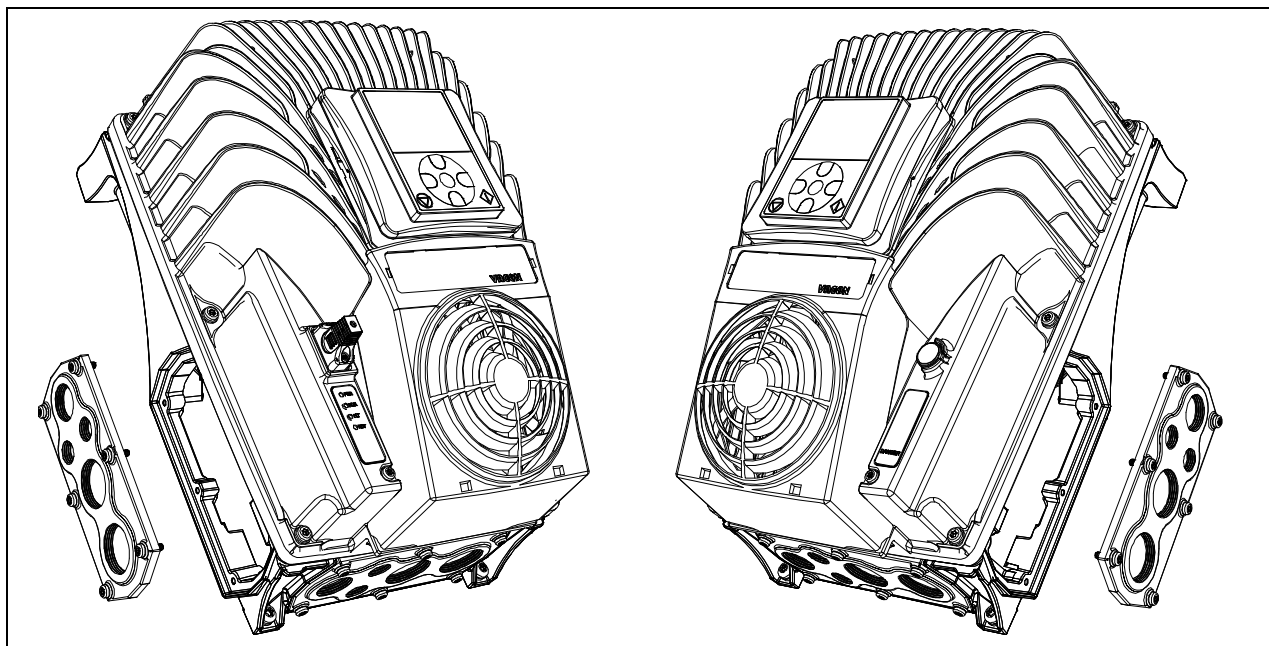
Débrancher la plaque d'entrée des câbles : exemple sur MM5
